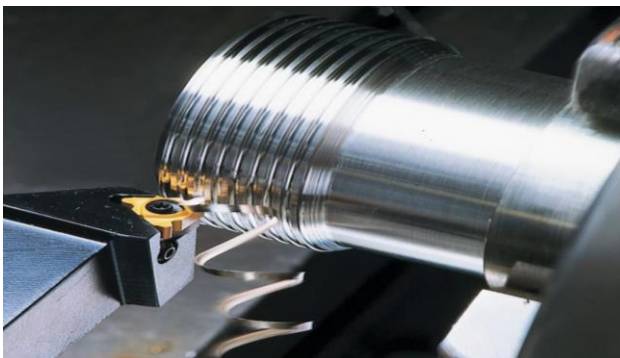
Точение резьбы на внешней и во внутренней поверхности заготовки
